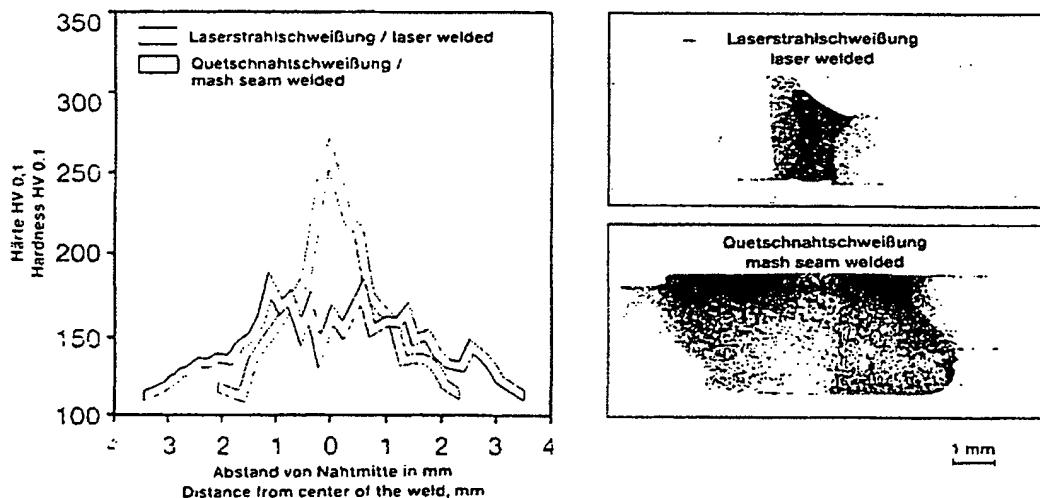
Nahtgeometrie und Harteverlauf der Laserstrahl- und Quetschnahtschweißung
